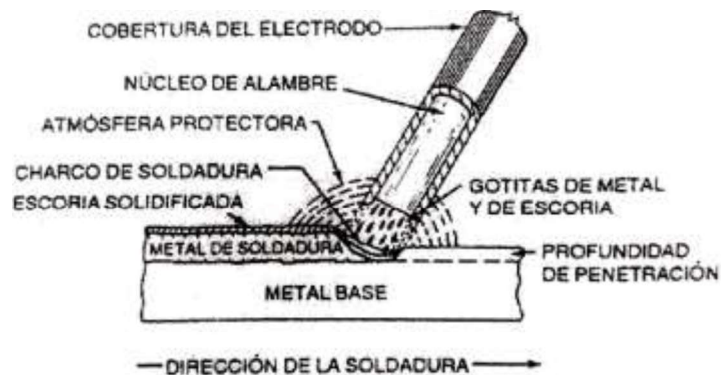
Soldadura por Arco Eléctrico.
